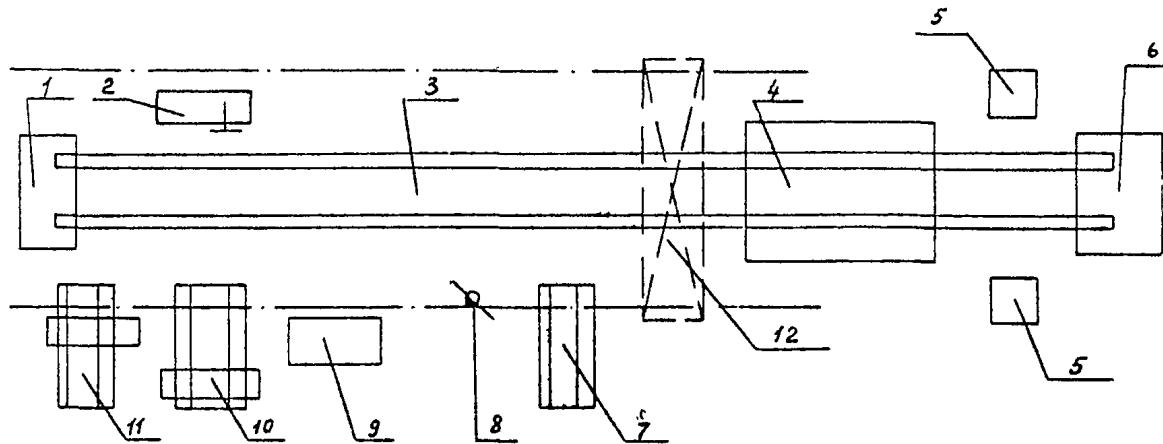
Рис. I. Типовая схема планировки рабочего места общей разборки автомобиля
